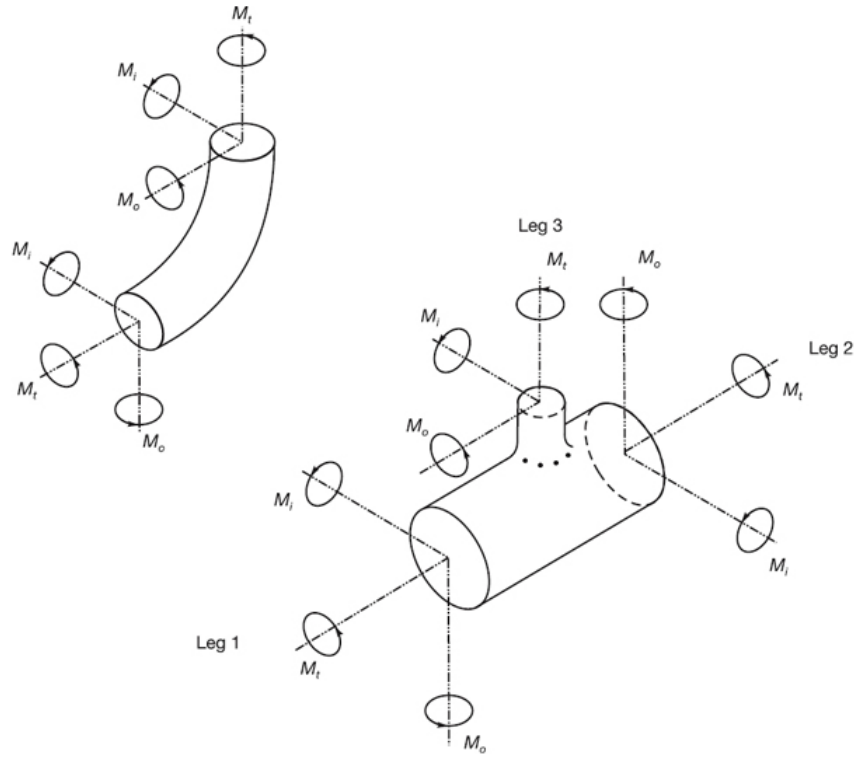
Momentos aplicados no plano e fora do plano do componente. (ASME B31.3, 2016)
